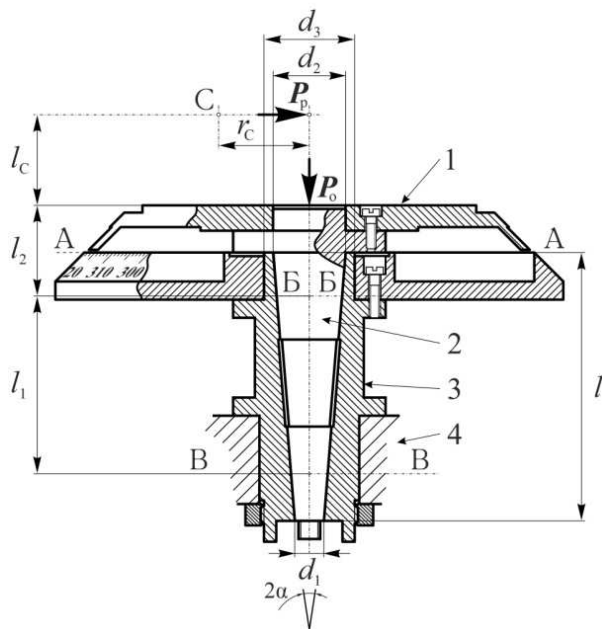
Варіант конічної опори підвісу, де: 1 – обертова платформа; 2 – конічна опора (цапфа); 3 – конічна опора (втулка); 4 – корпус
